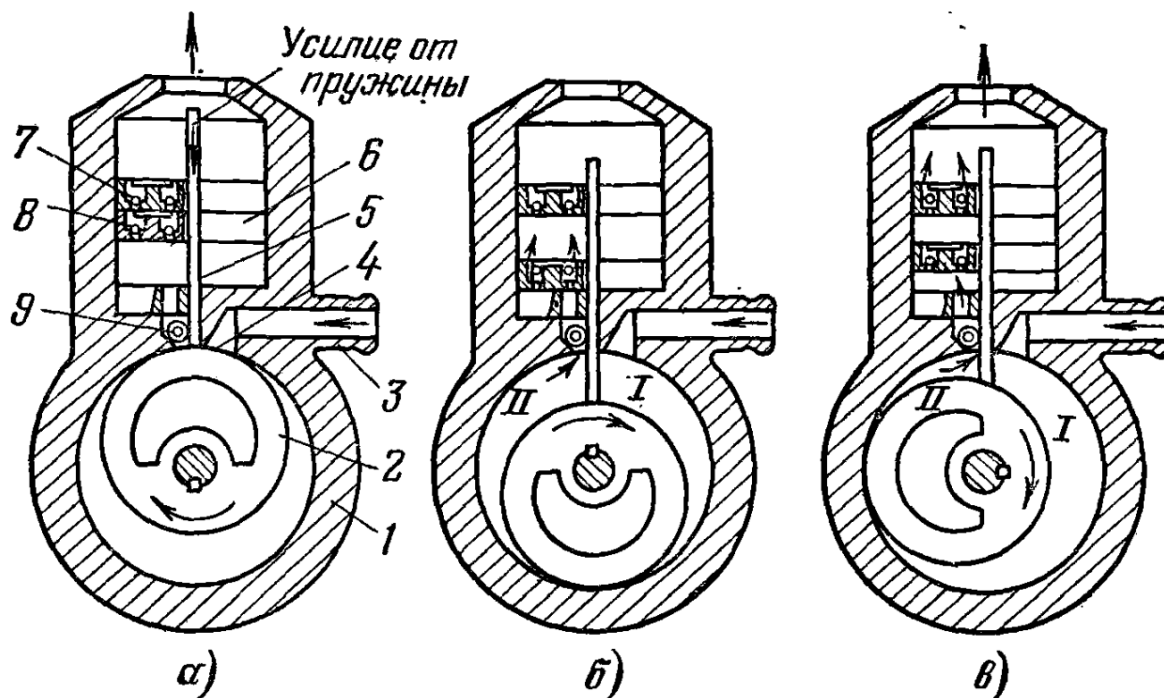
Схема пластинчато-статорного насоса с пластиной в виде поршня. 1 – цилиндрический корпус; 2 – эксцентрический ротор; 3 – входной патрубок; 4 – отверстие; 5 – пластина; 6 – поршень; 7 – выхлопной клапан; 8 – самодействующий клапан; 9 – ролик [8, с. 90]
